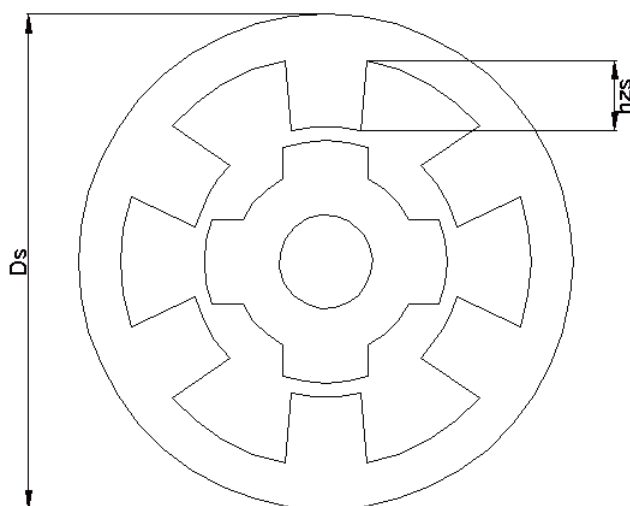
Внешний диаметр статора и высота полюса ротора, для трехфазного ВРД конструкции 6/4
